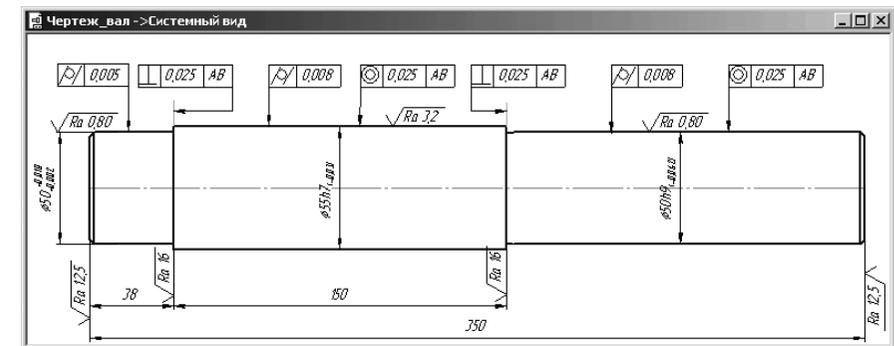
Вал с знаками обозначения шероховатости и допуска формы
